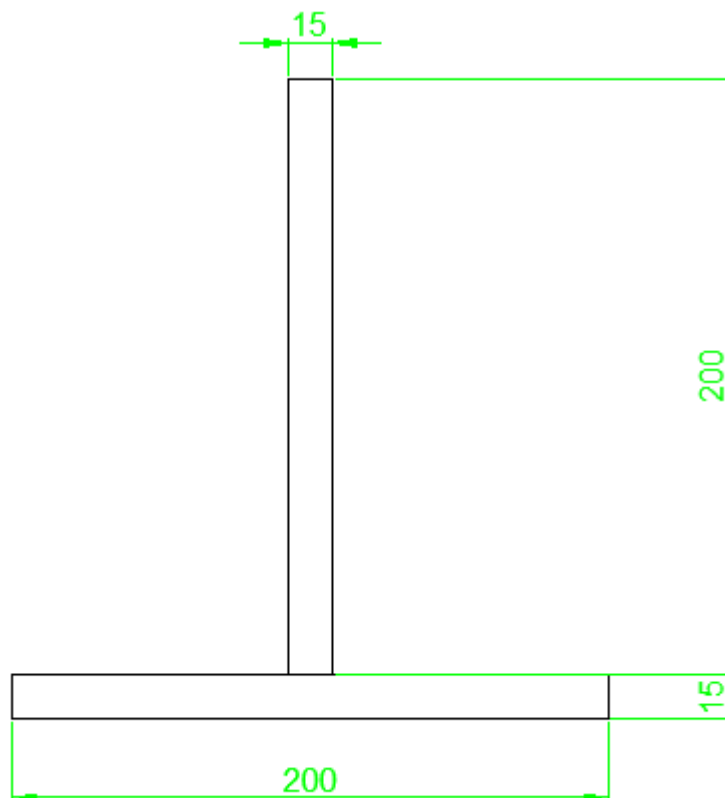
Corpo de prova para junta em ângulo. Dimensões em mm.
